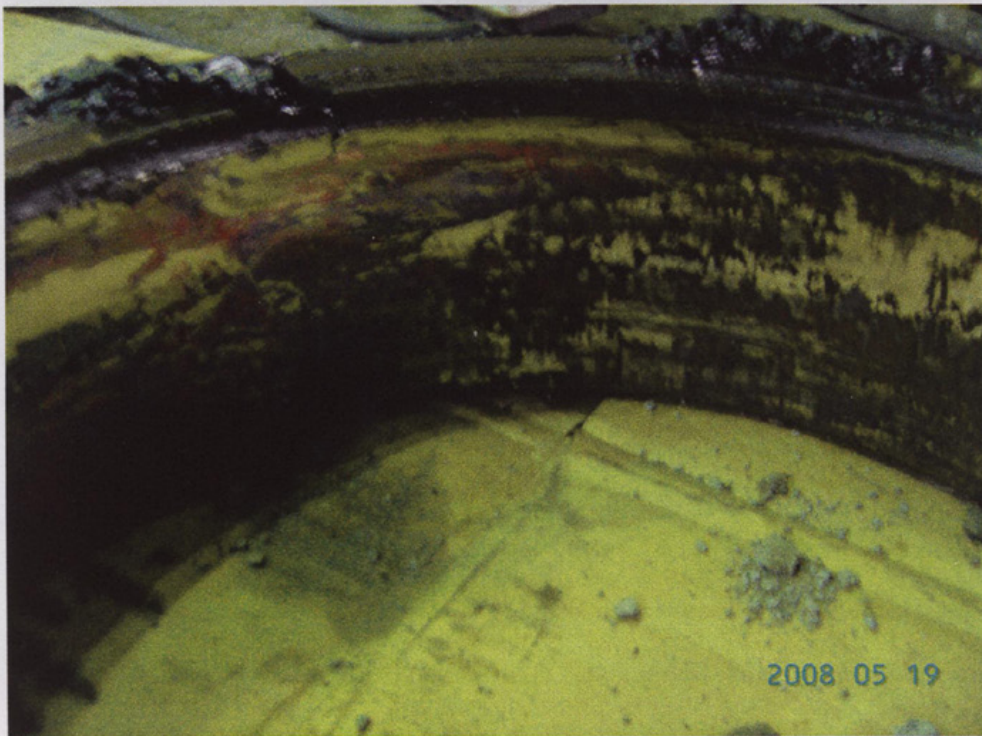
Наружное кольцо подшипника со смазкой Литол 24.
